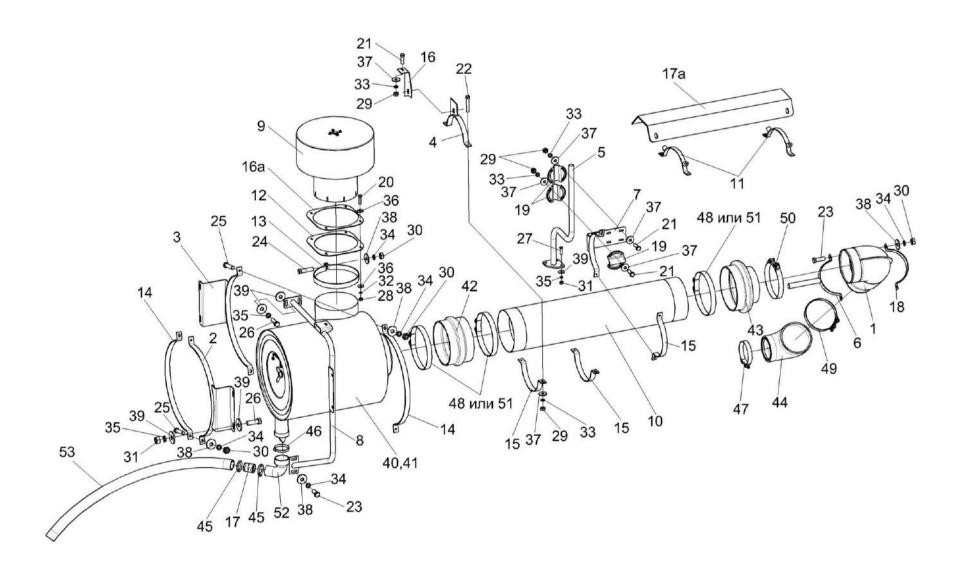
Установка воздухоочистителя КВК 0153000
